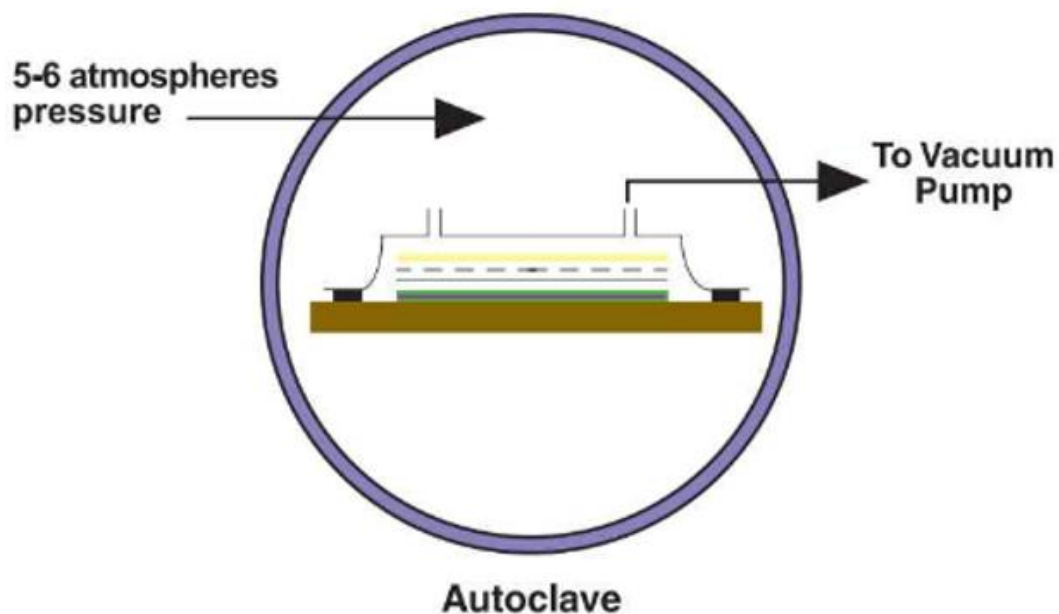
Moldagem de pré-impregnados com autoclave [6]
